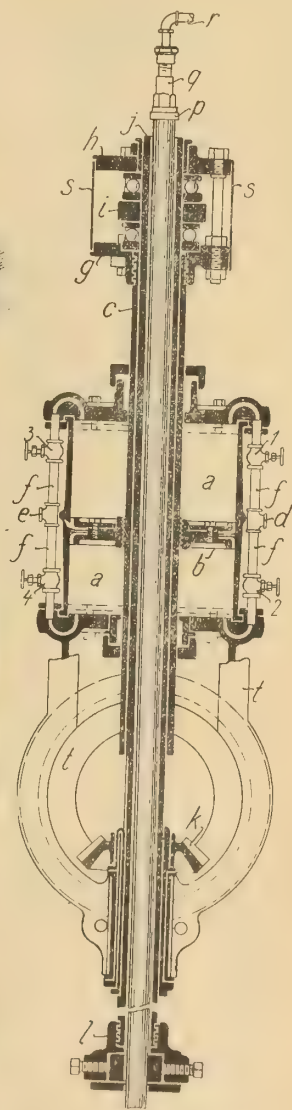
Hydraulischer Nachlaßapparat einer größten Schürfbohrmaschine der Sullivan Machinery Co. Chicago.
